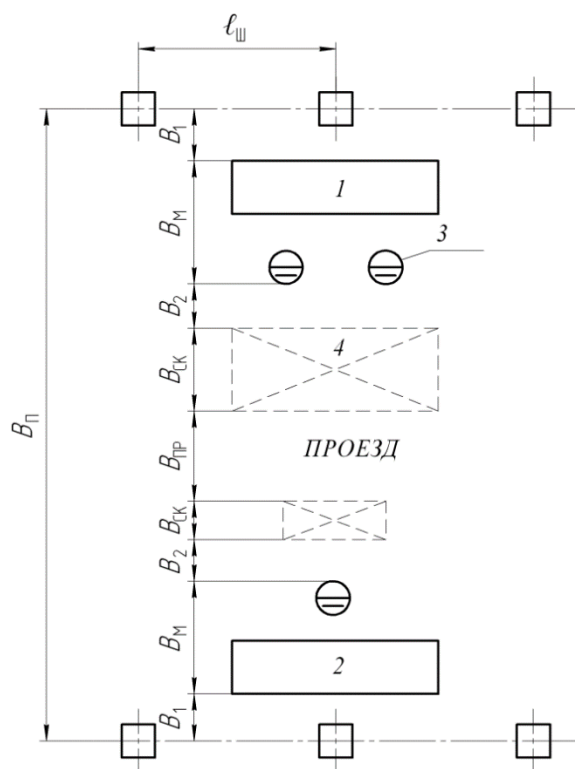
Схема планировки цеха при расположении складочных мест вдоль ряда (проезда): 1 – стенд для испытаний; 2 – сборочно-сварочный кантователь; 3 – место обслуживающего персонала; 4 – складочное место
